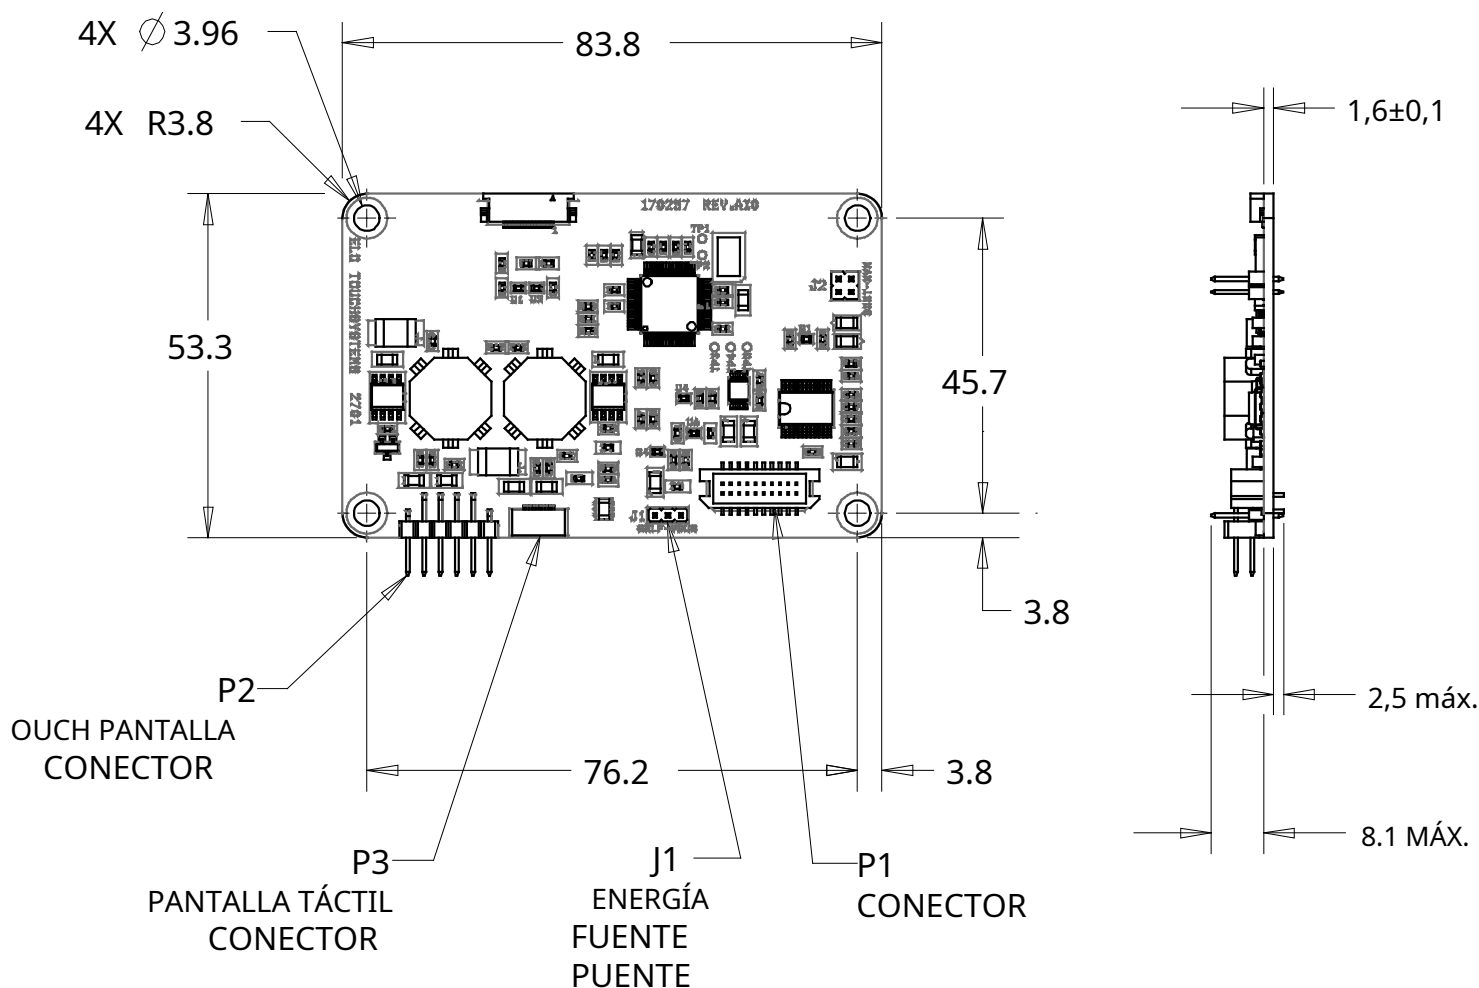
Dimensiones del 2701: vistas frontal y lateral (CTR-270100-IT-RSU-00R)
